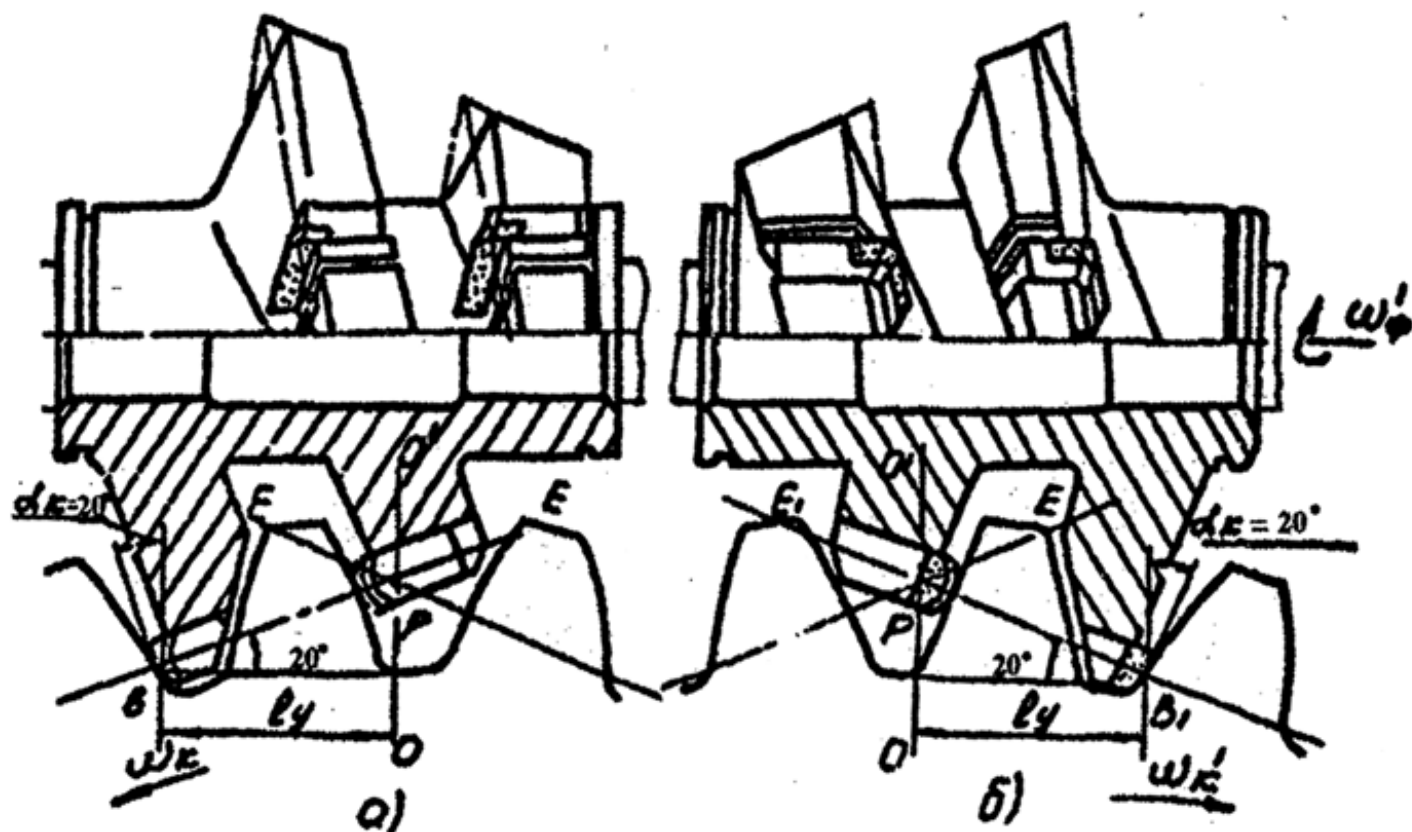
Схема зубофрезерования одним корпусом фрезы «Победа».
